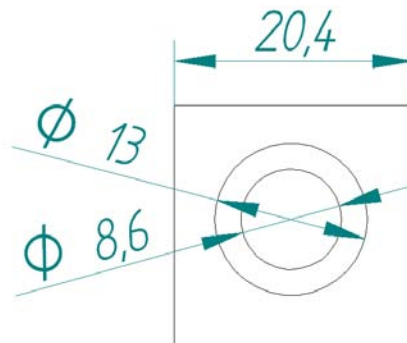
Croquis del plano de planta de la columna de burbujas en mm.
